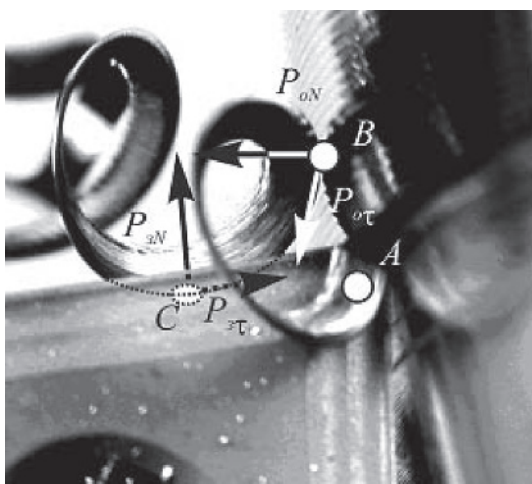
Контакт стружки в форме винтовой спирали с обрабатываемой и задней поверхностями
